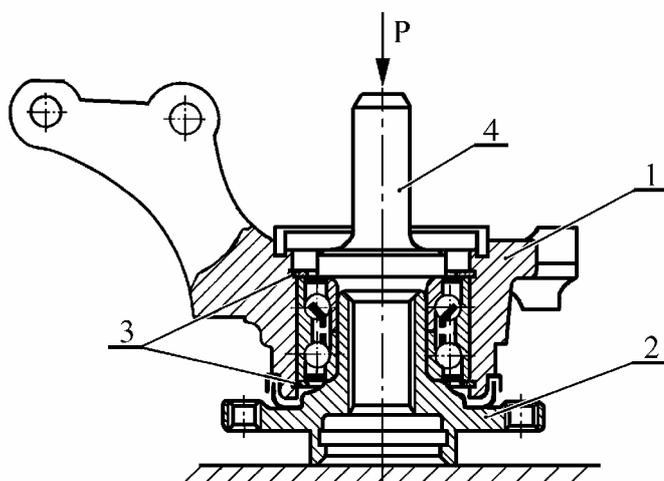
Напрессовка подшипника на ступицу переднего колеса:
